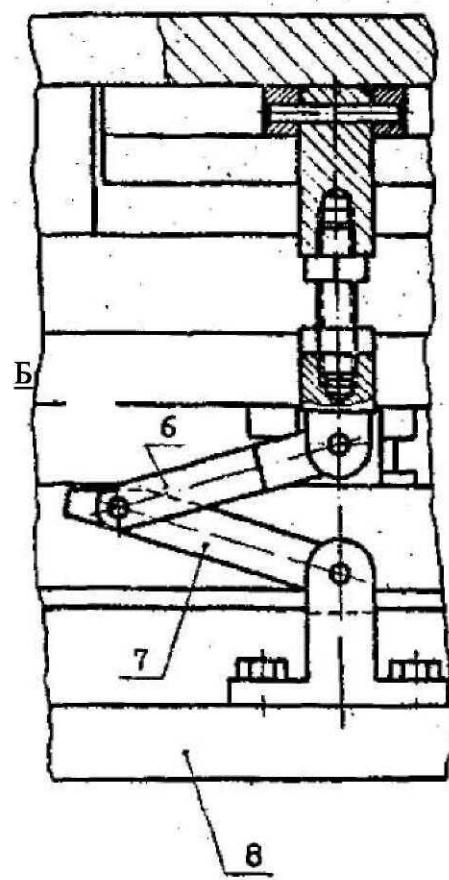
Пресс-форма для изготовления деталей методом прессования:
